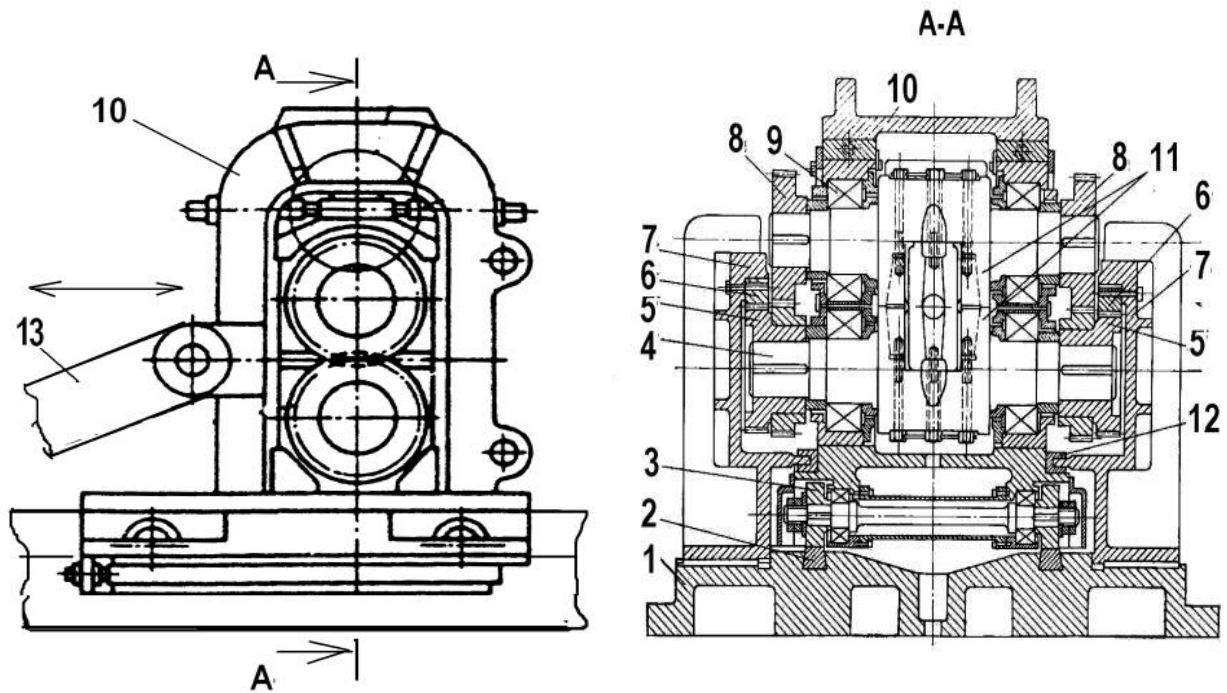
Робоча кліть стану холодного прокатування труби з рухливою станиною: 1 – рама; 2 – брус; 3 – ролик; 4 – шпindelь; 5 – шестерня; 6 – зубчасті рейки; 7 – припливи напрямної; 8 – зачеплення; 9 – підшипники; 10 – станина рамного типу; 11 – робочі валки; 12 – планки; 13 – ричаг
